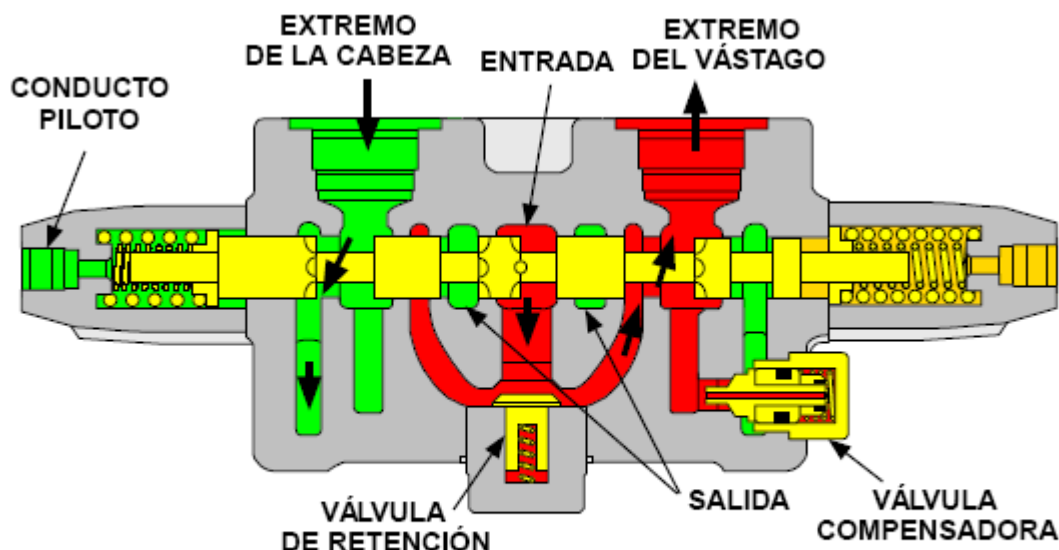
Válvula de control de levantamiento en posición BAJAR
